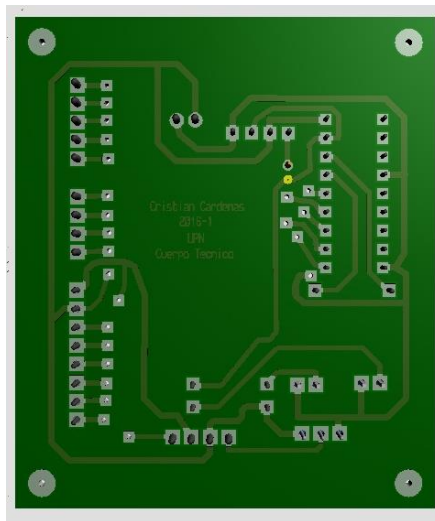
Vista Inferior 3D módulo Cuerpo Técnico
